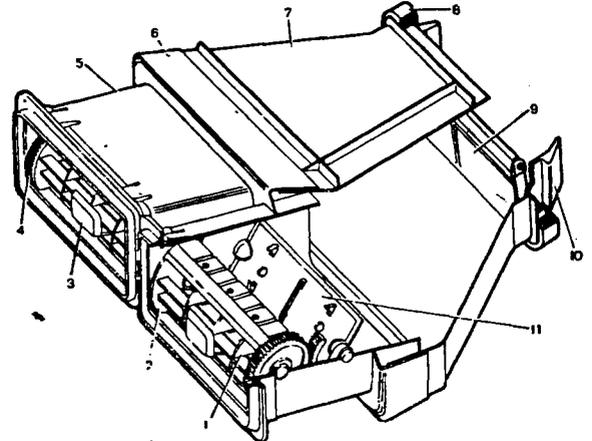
Центральные сопла вентиляции салона кузова: 1 - лопатка сопла; 2 - сопло; 3 - рычаг сопла; 4 - зубчатое колесо привода заслонки сопла; 5 - корпус сопла; 6 - задний уплотнитель трубы воздухопритока; 7 - труба воздухопритока; 8 - передний уплотнитель трубы; 9 - клапан трубы воздухопритока; 10 - защелка трубы воздухопритока; 11 - заслонка сопла с зубчатым сектором
